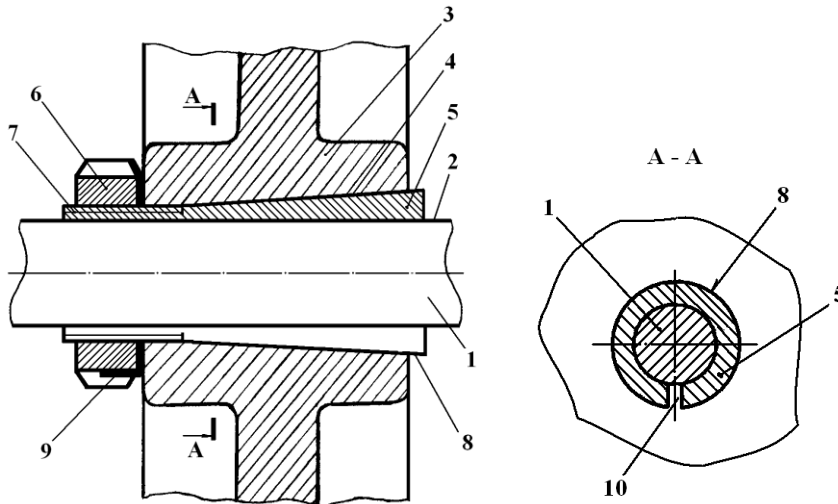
Схема безшпонкового фрикційного з'єднання деталі з валом
